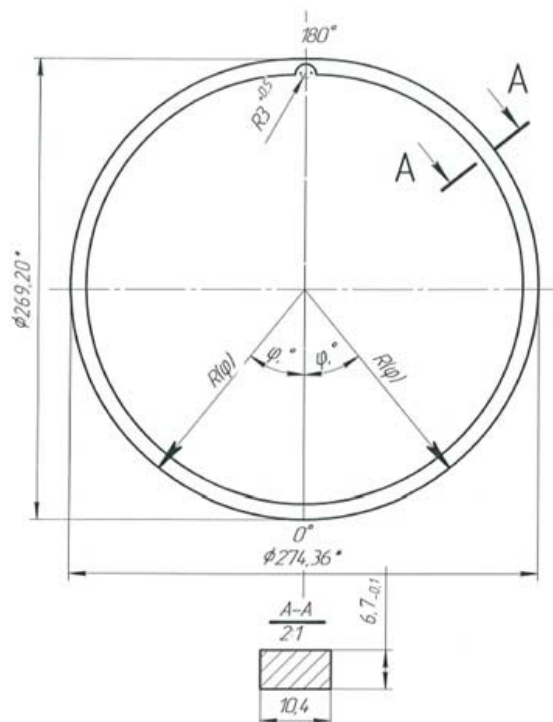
Форма заготовки поршневого кольца (на примере верхнего поршневого кольца промышленного дизельного двигателя Д49)
